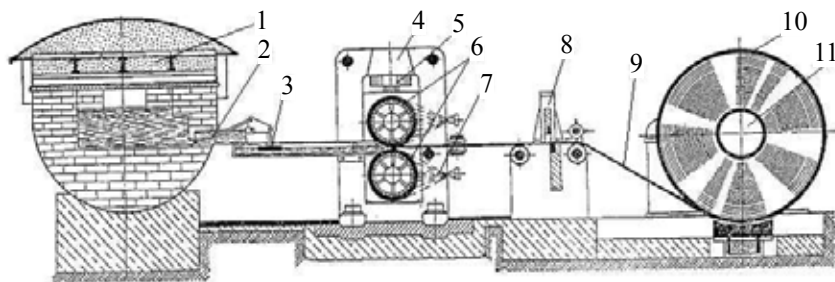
Агрегат непрерывного литья с подводом расплава сбоку
